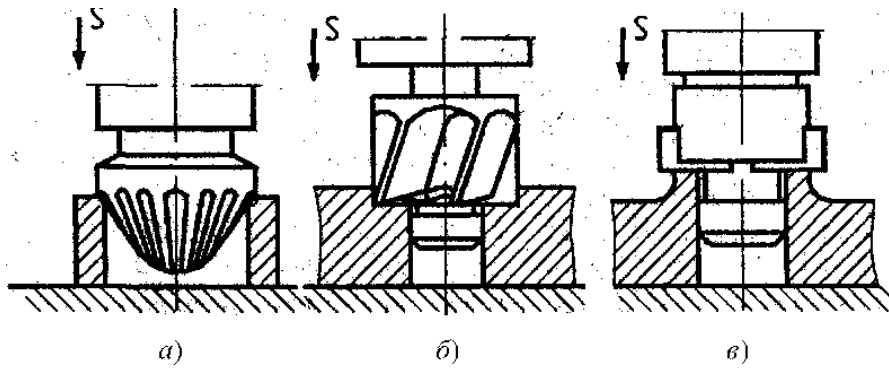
Обработка вспомогательных элементов в отверстиях: а – зенковками; б – цековками; в – цековками со специальными пластинами
